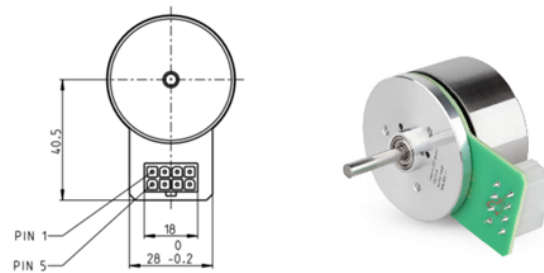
Motor EC 45, esquema a la izquierda, aspecto del motor a la derecha
